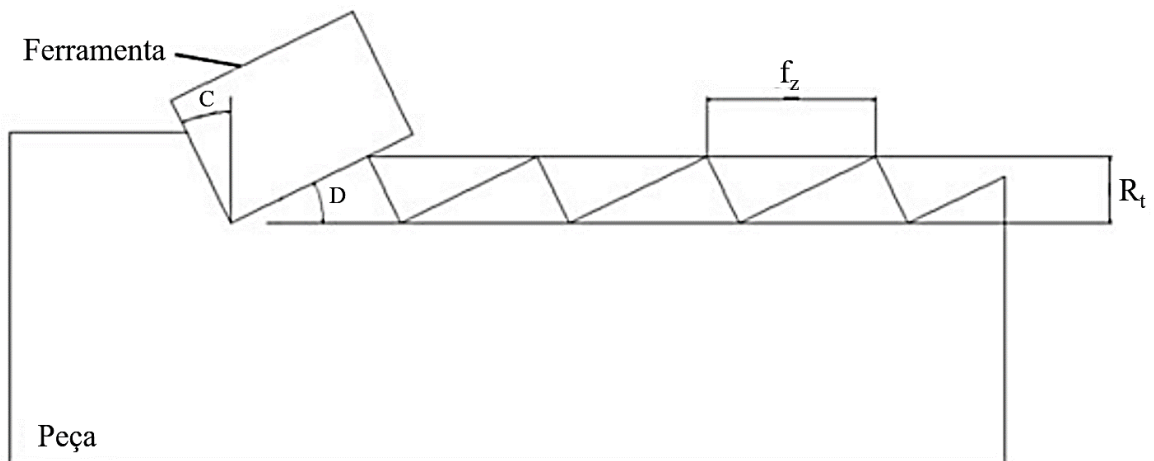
Perfil teórico de uma superfície usinada por fresamento frontal.
